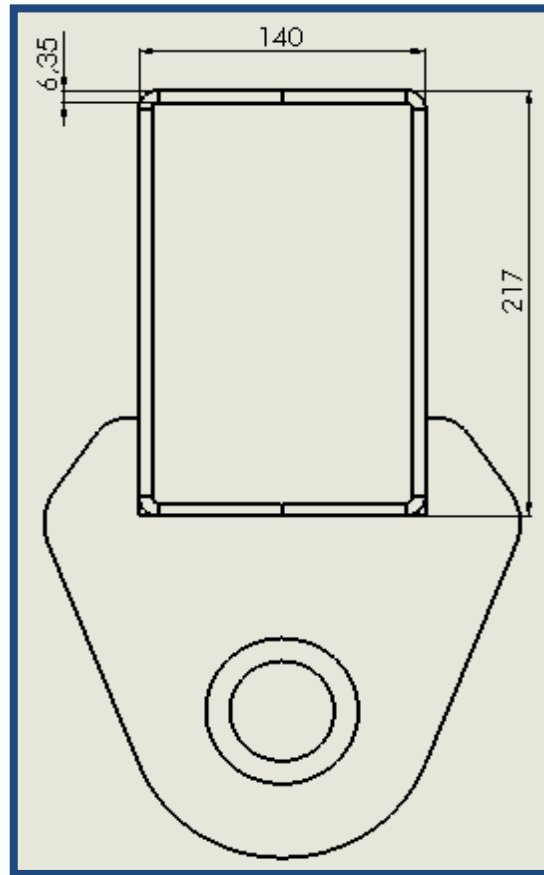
Dimensiones de la sección de viga sostén.
